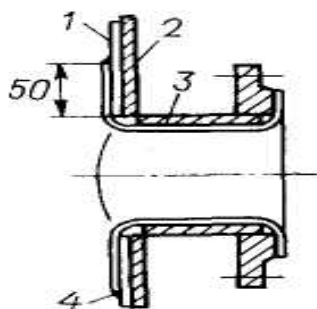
Защита штуцера полимерными материалами: 1—обкладка корпуса полимерным материалом; 2—корпус из углеродистой стали; 3—защита штуцера полимерным материалом; 4—сварка сплошным швом по периметру.
